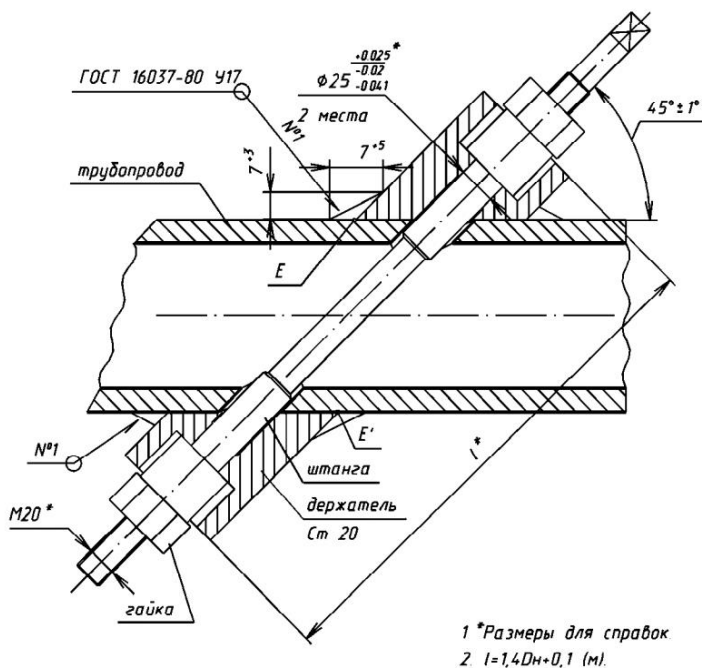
Схема приварки держателей ПЭП к трубопроводу
